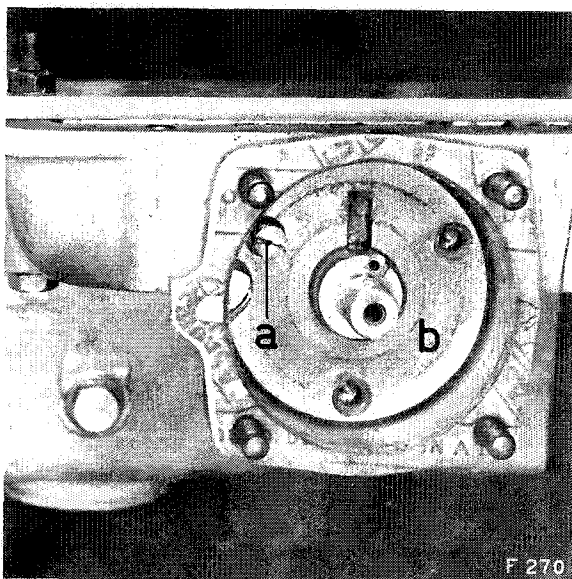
Lösen der Senkschrauben der Schaltkolbenführung
